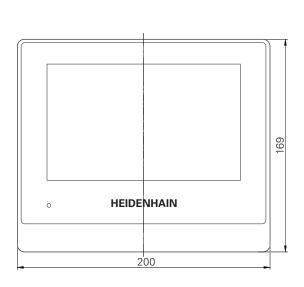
Размеры корпуса устройств с ID 1089181-хх
